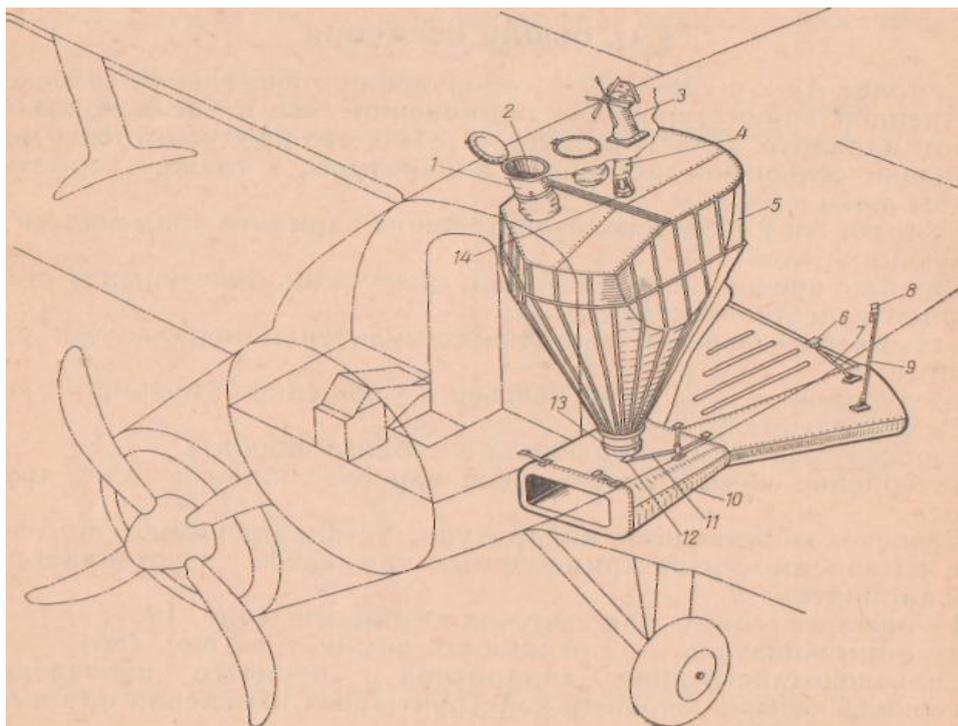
Схема установки опыливателя (выпуск 1959—1962 г.)
